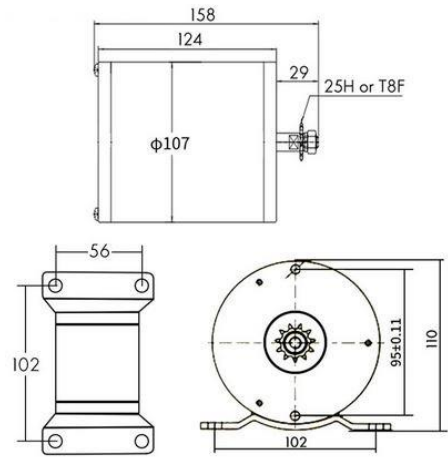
Электродвигатель Kunray и его габаритные размеры
